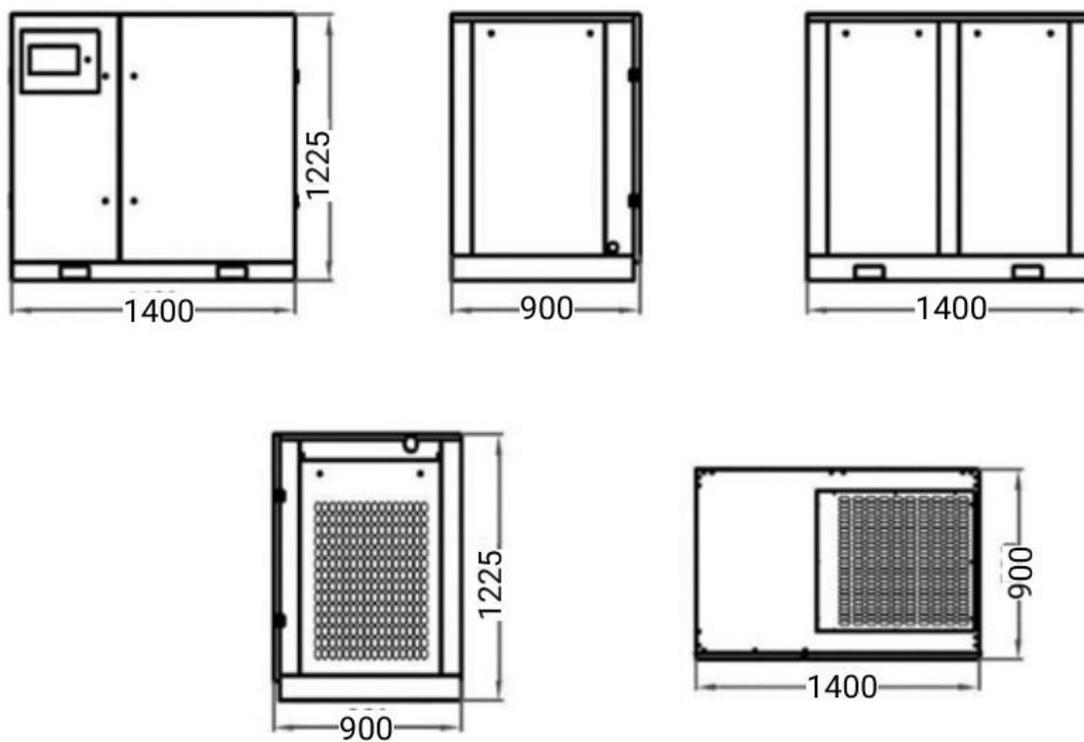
Габаритные размеры компрессора BRM-30A
